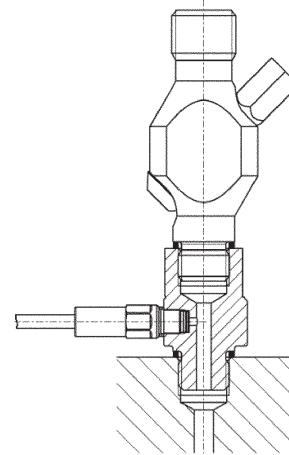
Einbaubeispiel: Sensor eingebaut unter dem Indizierventil mit Adapter 6582A1
